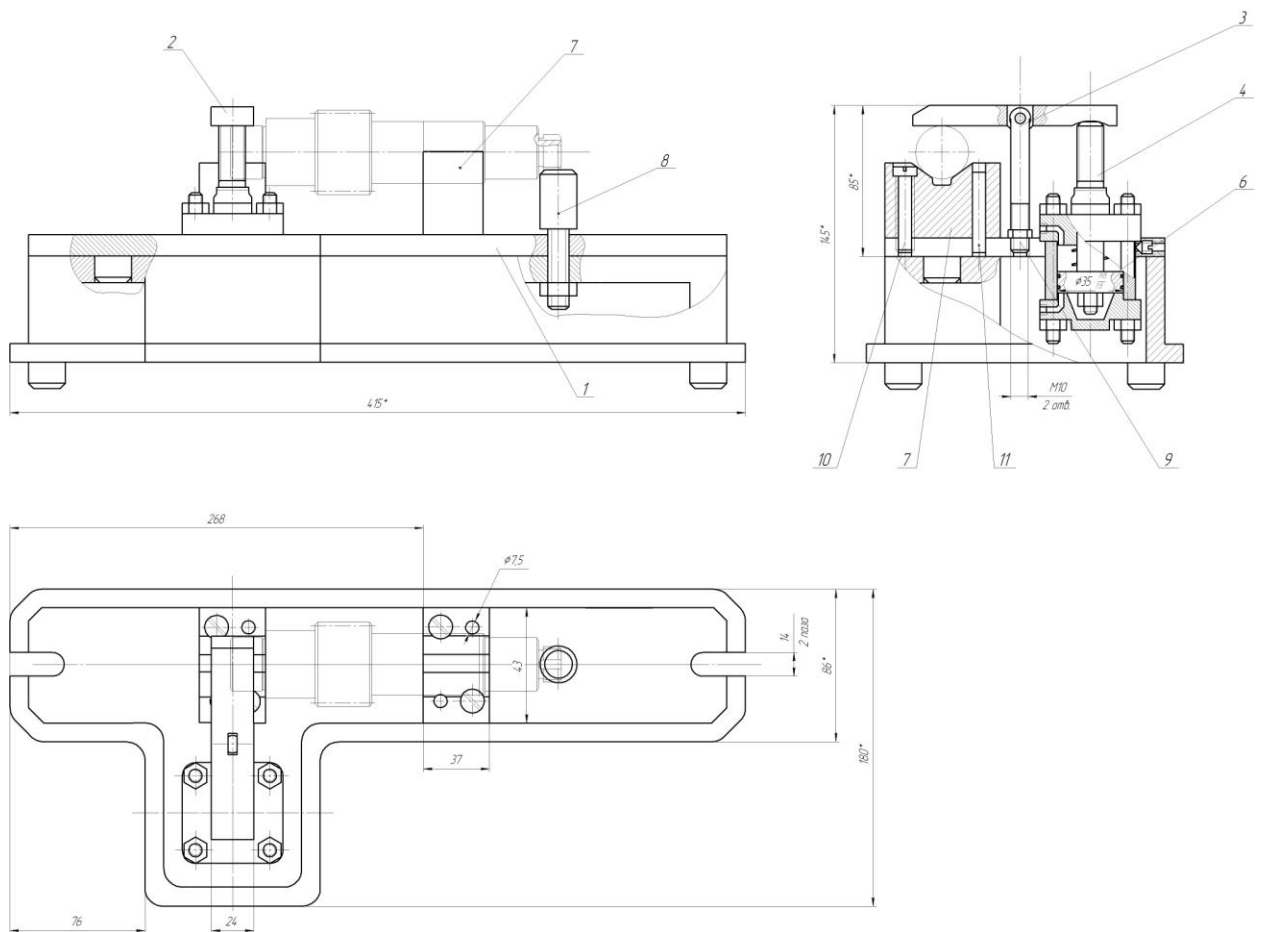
Приспособление для шпоночно-фрезерной операции
